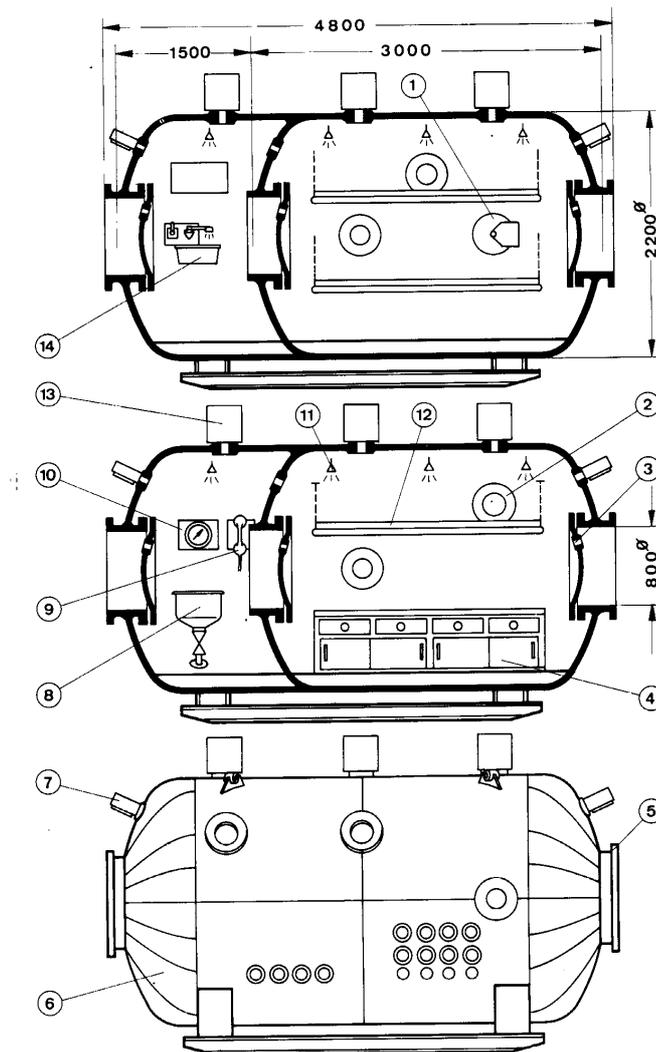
Dimensiones y elementos de una cámara de descompresión estándar, de un sistema de buceo profundo.
